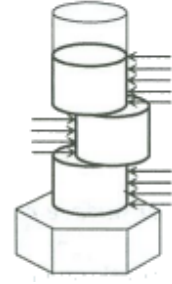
Plans de cisaillement d'un corps de boulon
